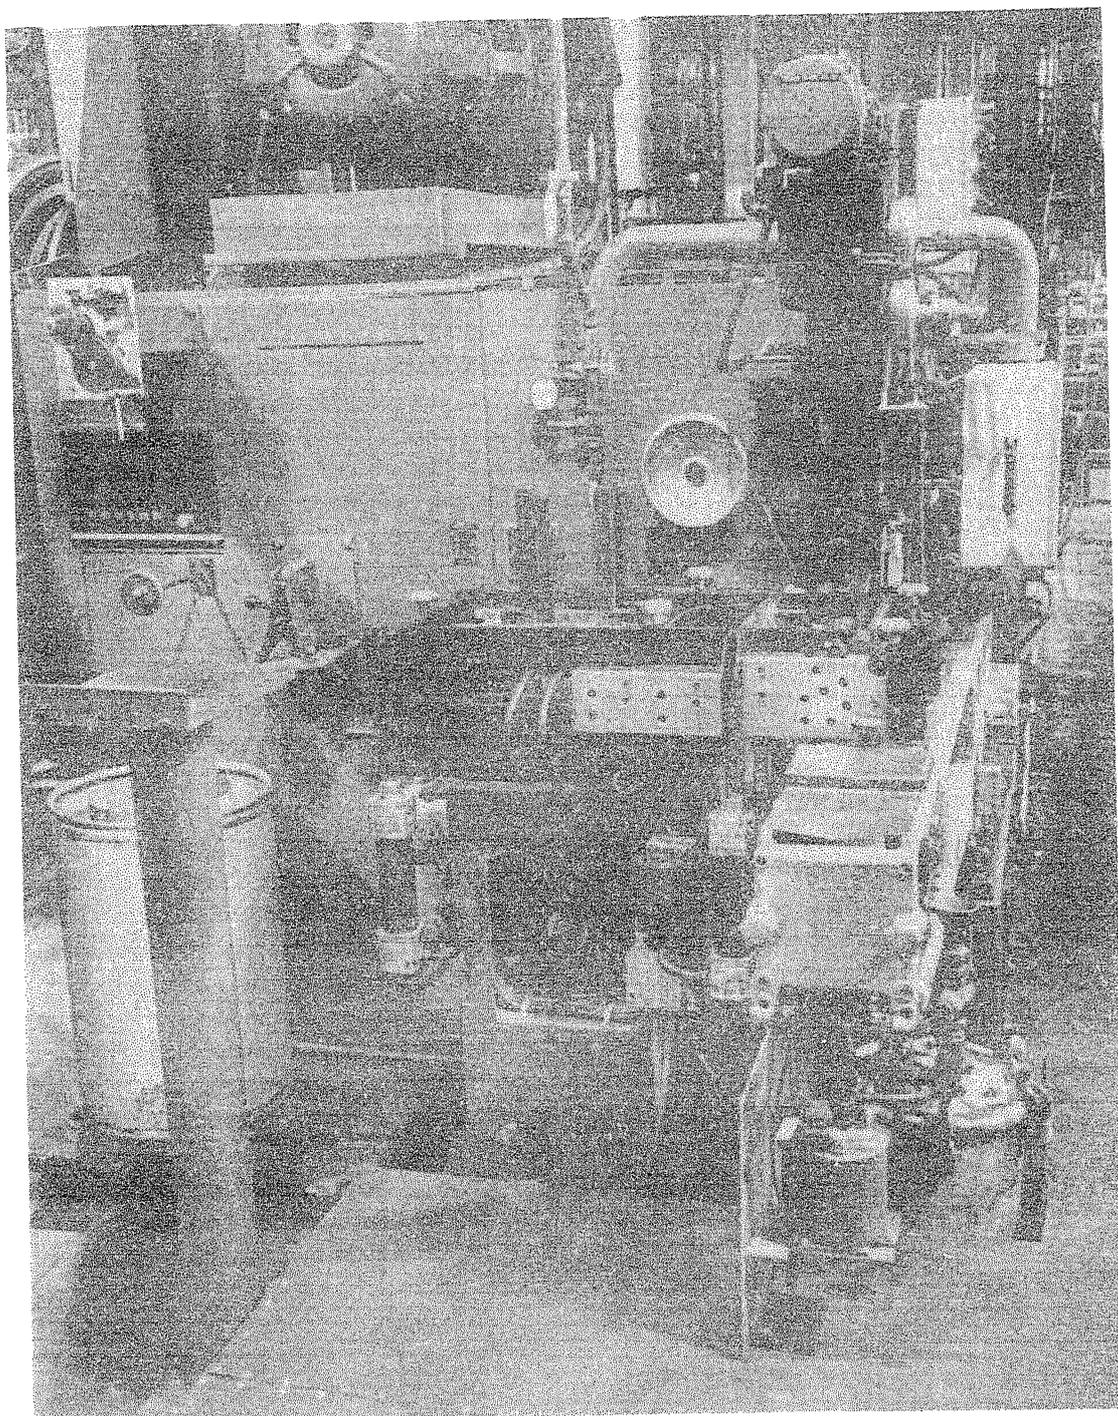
b Vista Lateral Izquierda de la soldadora.
